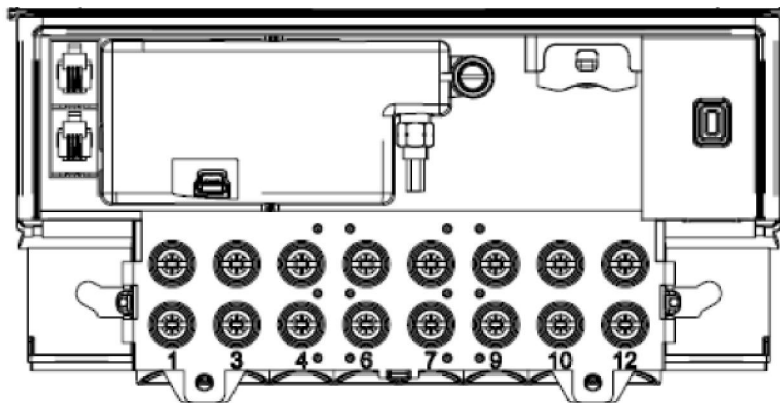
Rysunek gabarytowy - poglądowy widok z boku
